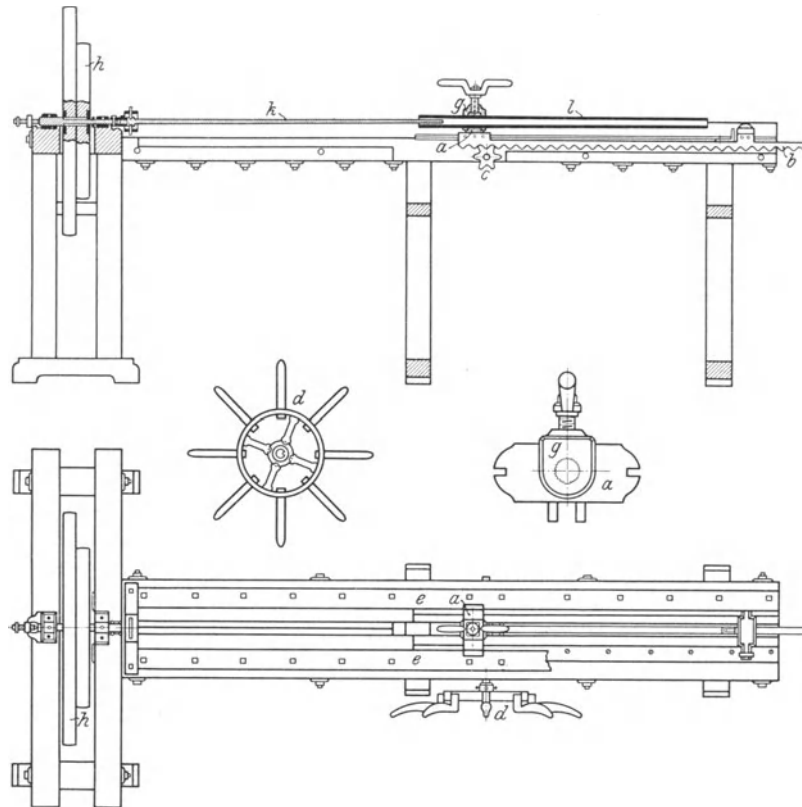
bis 23. Maschine zum Ausbohren der überlappt geschweißten Läufe.
